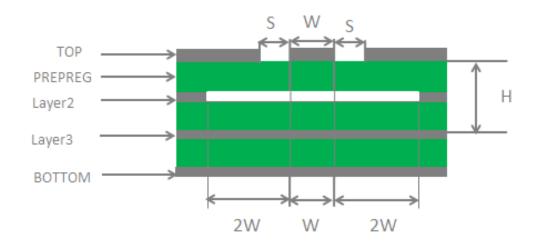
四层 PCB 板共面波导结构(参考地为第三层)
